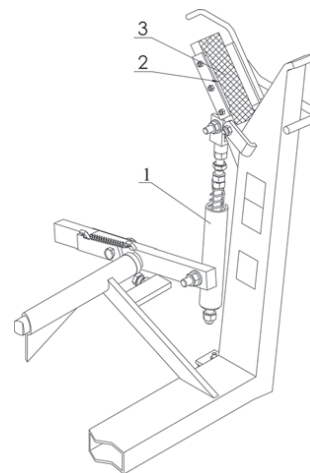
Cortador de la película: 1 - unidad tensora, 2 - cuchilla de corte, 3 - sujeción.
